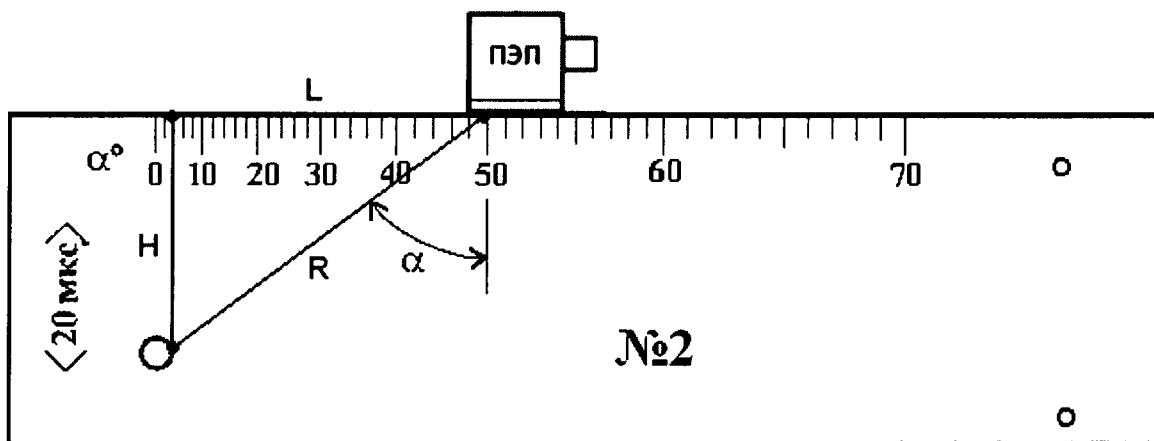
Контрольный образец №2 из комплекта КОУ-2
